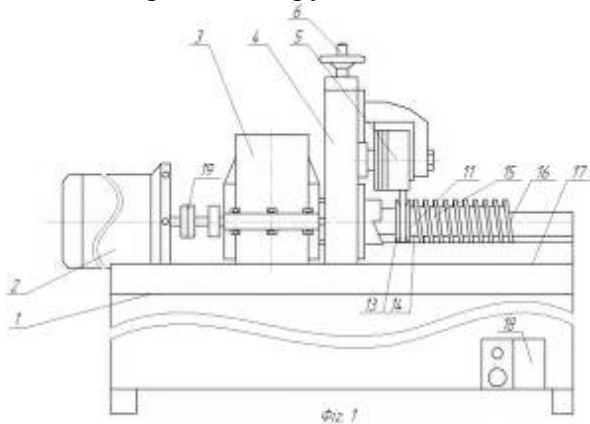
Верстат для виготовлення гвинтових гофрованих заготовок
